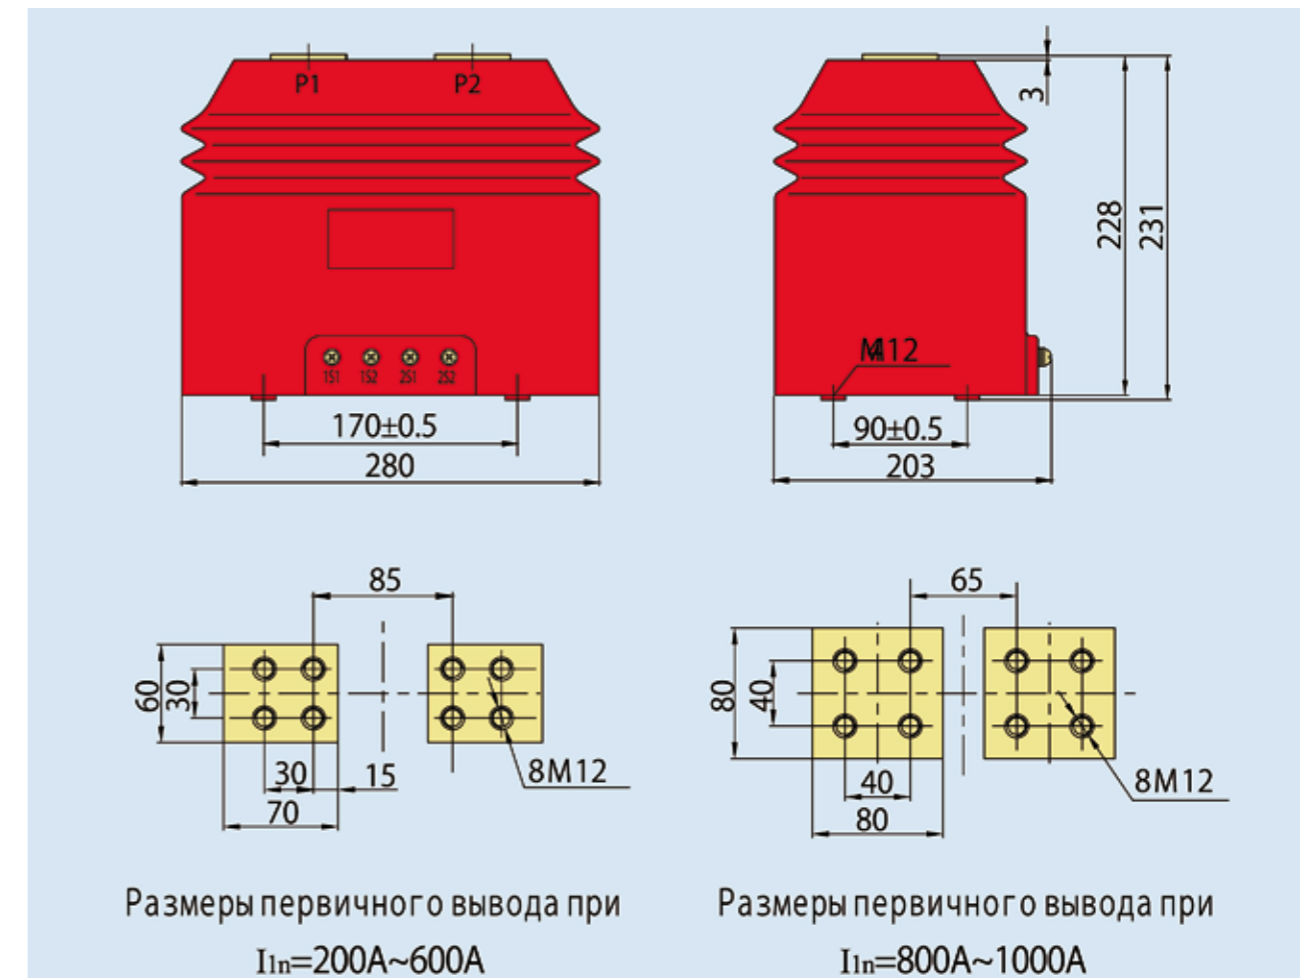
Внешний вид и размеры трансформатора тока LZZJ-10
